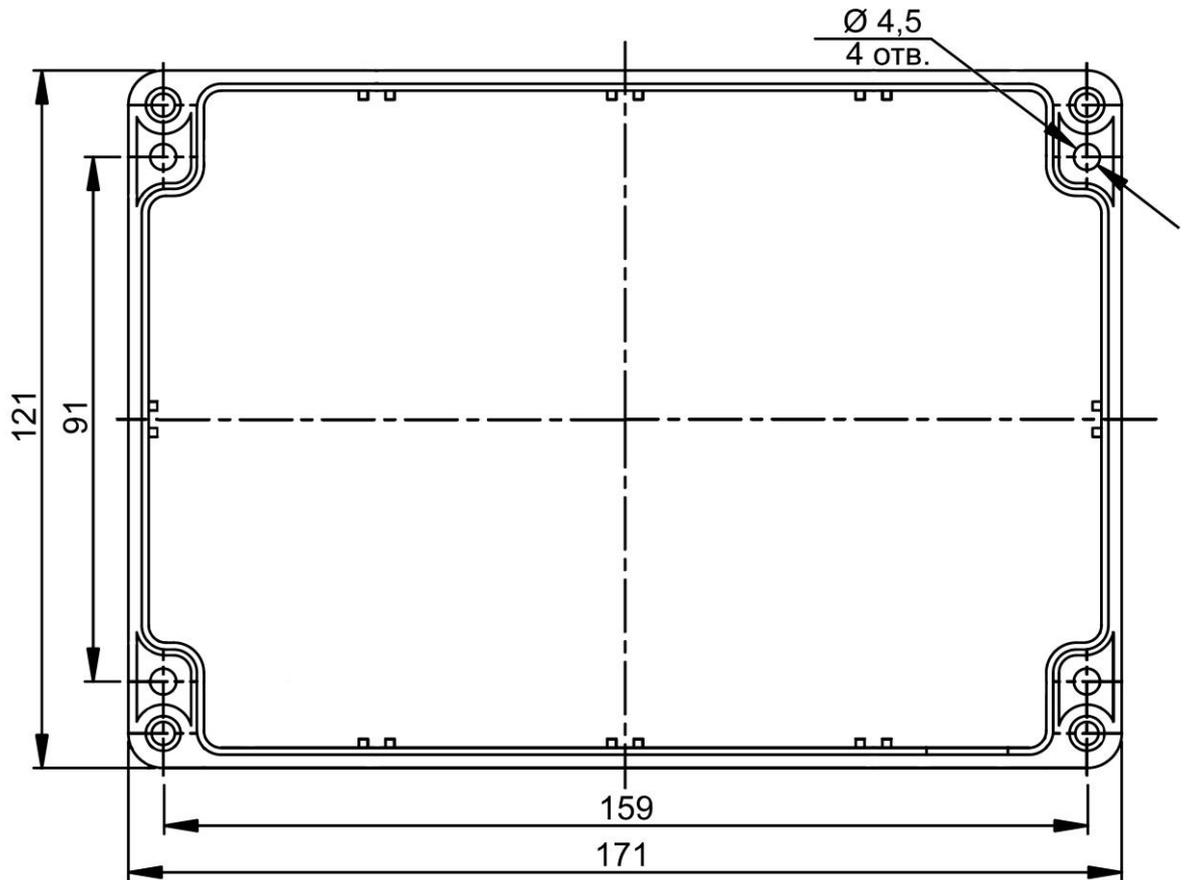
Размеры монтажного бокса и расположение крепежных отверстий
